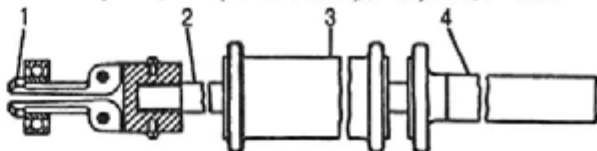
Съемник 7823-6090 для выпрессовки подшипника из коленчатого вала:
